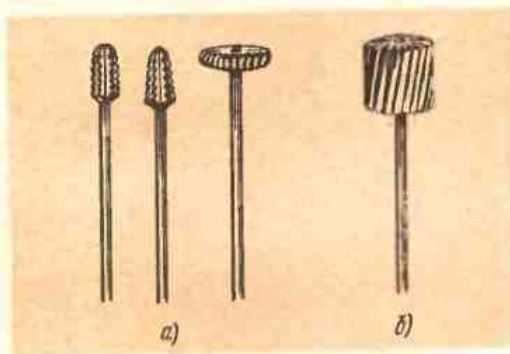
Фрезы шлифовальные: а — зуботехнические, б — самодельная (шарошка)
